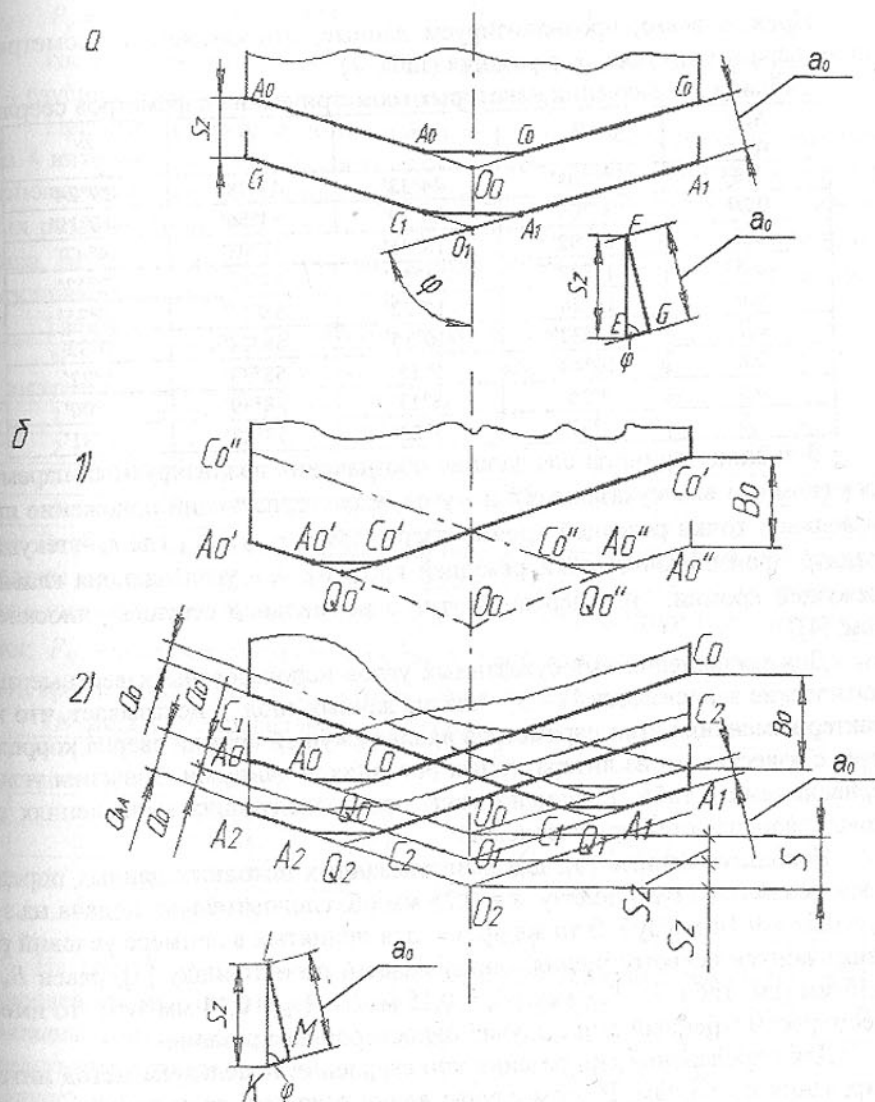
Определение толщины среза при сверлении: а - при симметричной заточке сверла; б - при асимметричной заточке сверла, $B_o \geq s_z$; б₁ - исходное положение; б₂ - положение режущих кромок после поворота сверла на пол-оборота и 1 оборот
